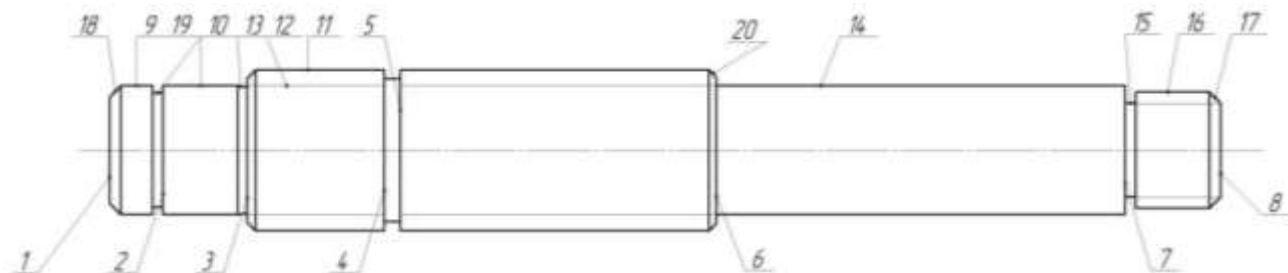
Ескіз деталі «Вал шліцевий»
